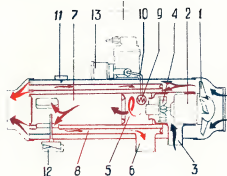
Бензиновый отопитель, работающий независимо от двигателя: 1 — вентилятор подогреваемого воздуха; 2 — электродвигатель; 3 — впускной патрубок; 4 — нагнетатель воздуха для горения; 5 — форсунка; 6 — выпускной патрубок; 7 — основная камера горения; 8 — теплообменник; 9 — свеча накаливания; 10 — топливотопляющая трубка; 11 — датчик перегрева; 12 — температурный переключатель; 13 — магнитный клапан; 14 — регулятор подачи топлива.
